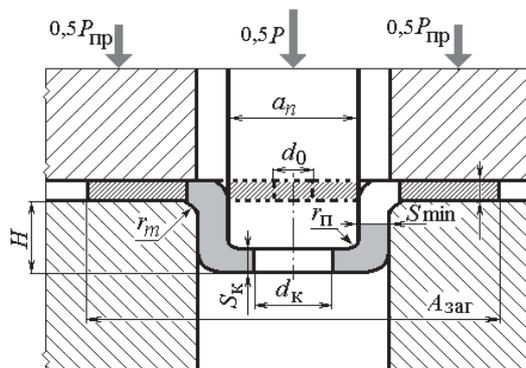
Схема совмещенного процесса вытяжки-отбортовки
